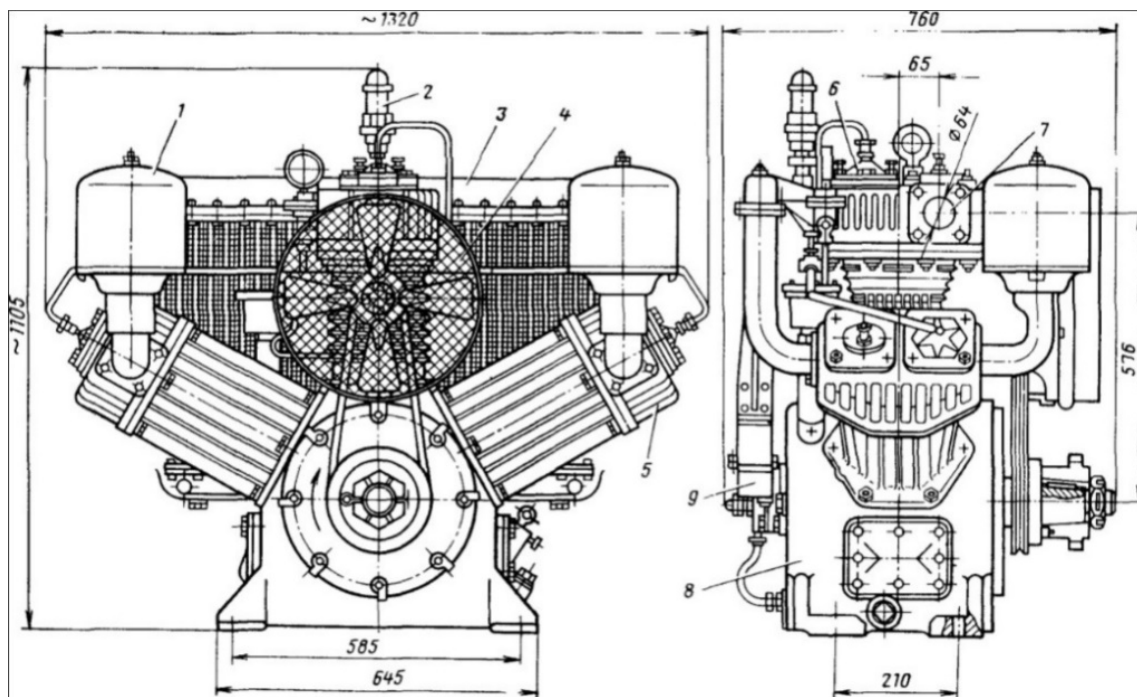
Общий вид компрессора КТ-6, КТ-7
